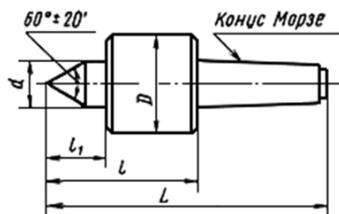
Задний центр с Конусом Морзе 3 для станка Haas ST-10Y с ЧПУ
